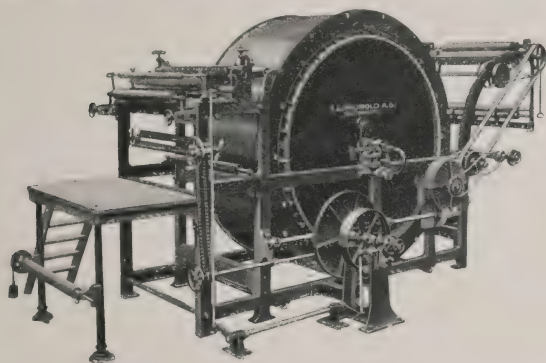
Spezial-Maschine für Füll-Appretur mit Doppel-Rakel (Haubold)
